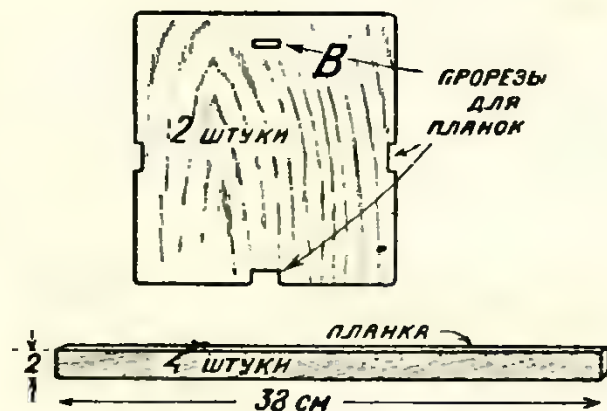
Вверху: вид боковины; внизу: размеры планки.
